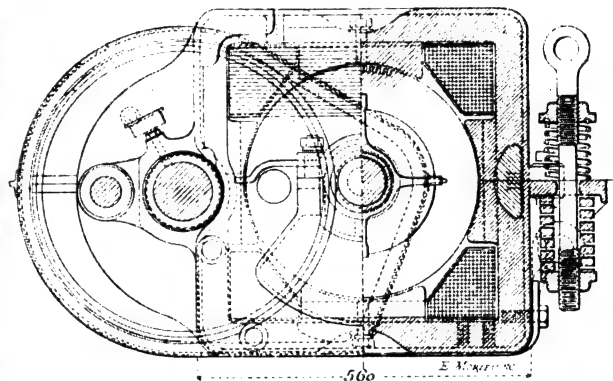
Moteur de tramway de 20 chevaux. Coupe transversale et vue par bout.
